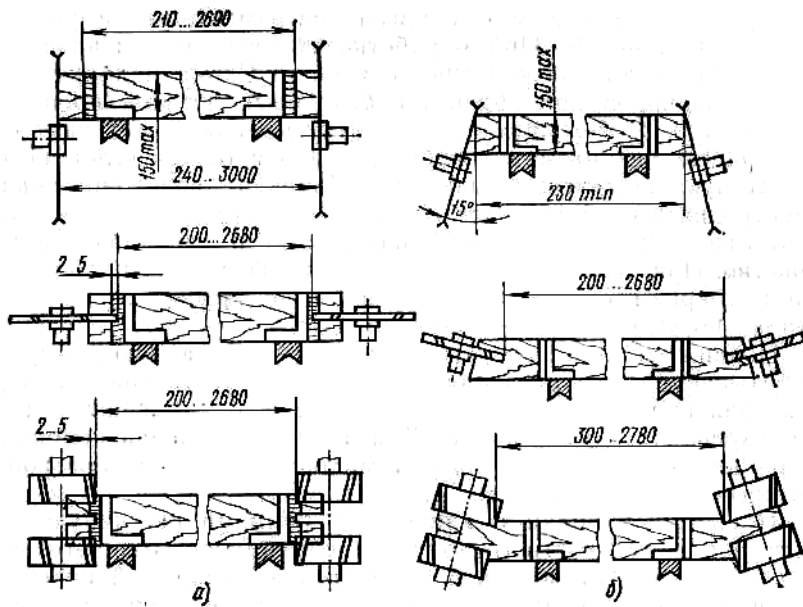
Наладка двустороннего шипорезного станка с использованием подпоров-вкладышей (а) и без подпоров (б)
